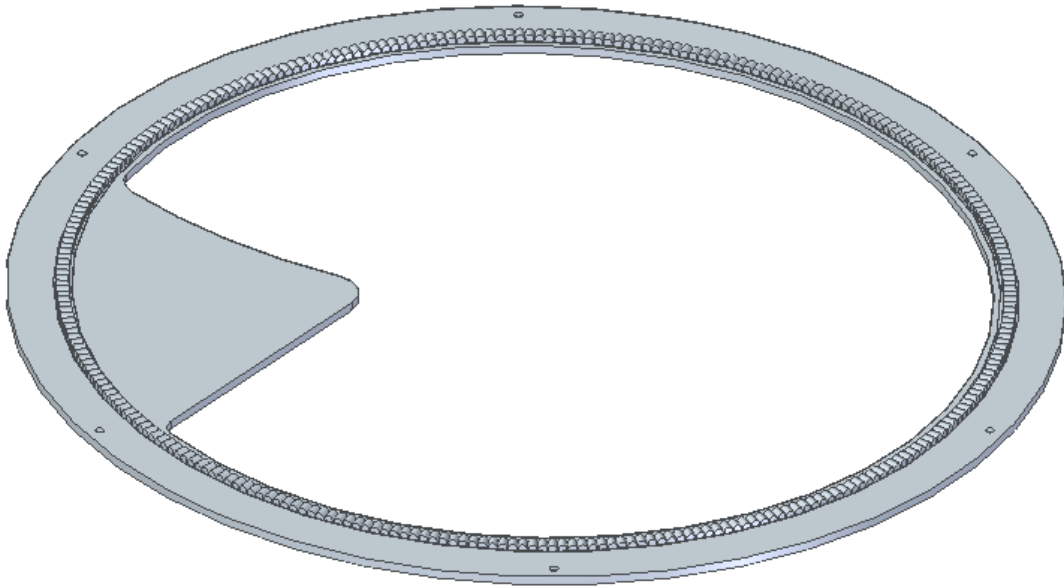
Placa fija con los rodamientos de rodillos
